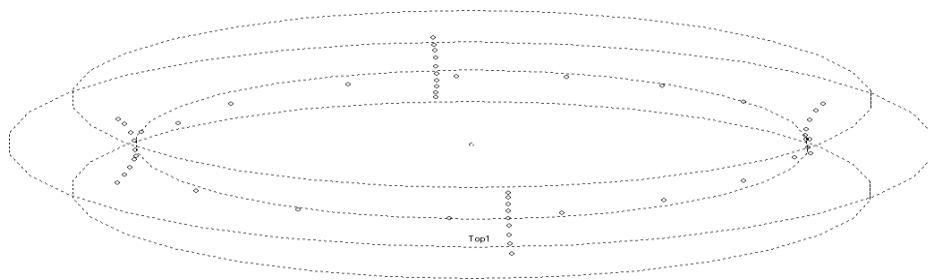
Вимірювання тороїдальної поверхні
